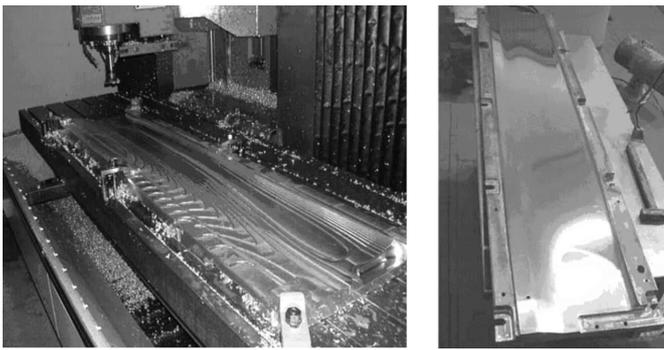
Изготовление формообразующей матрицы лопасти РВ
